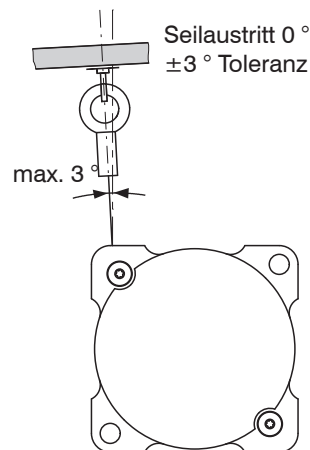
Befestigung und maximaler Schrägzug des Messseils
